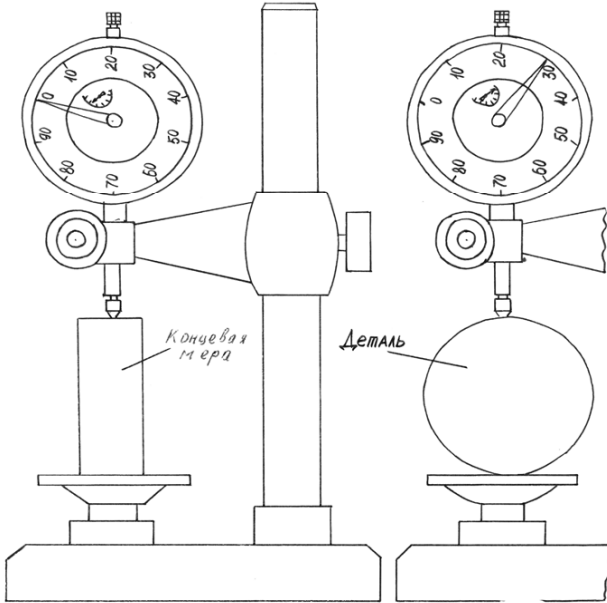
Вимірювання зовнішнього розміру: а – встановлення на “нуль”; б – вимірювання діаметра вала
